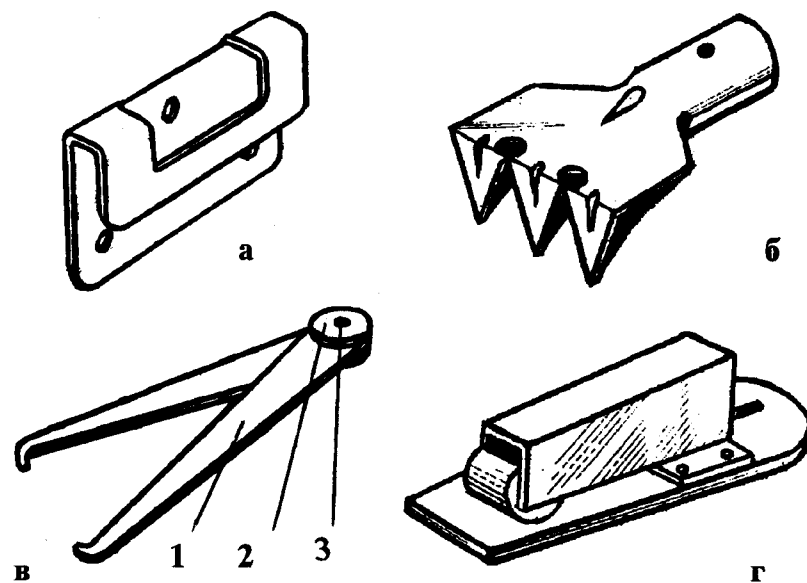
Изделия из сортового проката: а — ручка для дверки шкафчика, ящика; б — рыхлитель; в — нутромер: 1 — ножка; 2 — шайба; 3 — ось; г — зажим для таблиц
